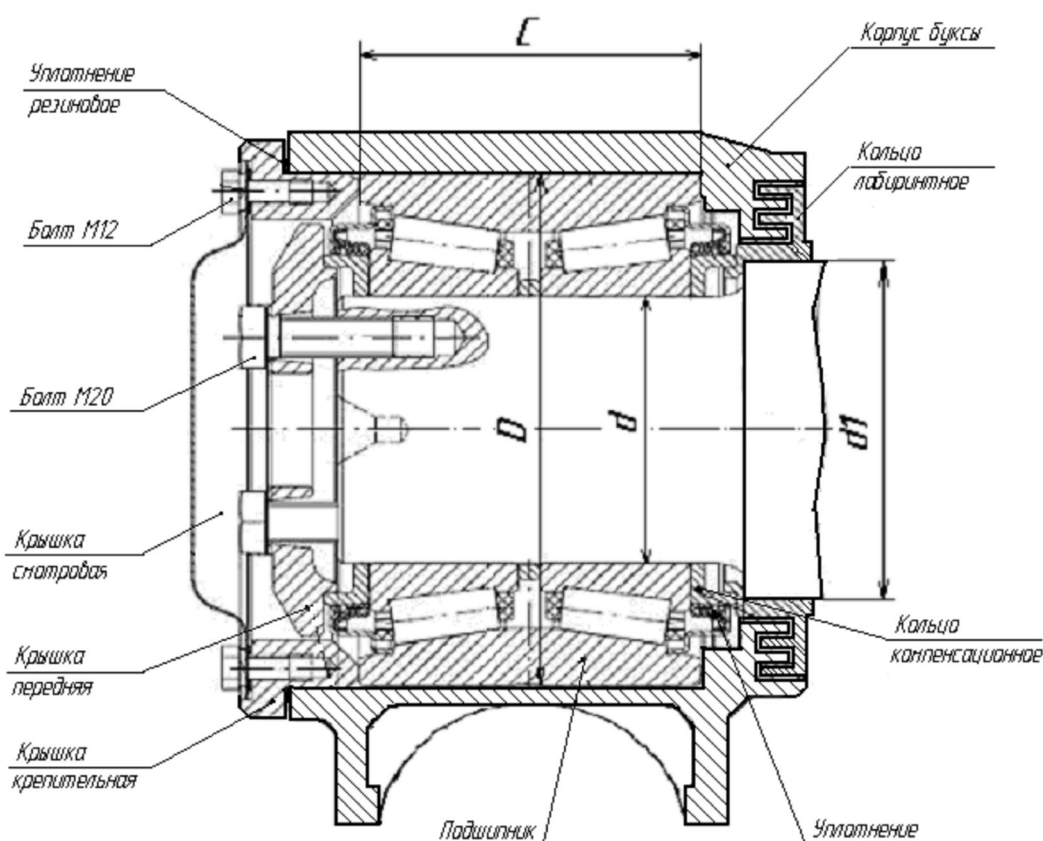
Подшипник кассетного типа в габаритных размерах 130x250x160 мм торговой марки Бренко
